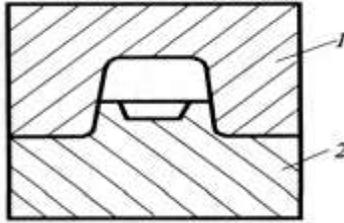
Штамповка в закрытом штампе: 1, 2 – верхняя и нижняя части штампа
